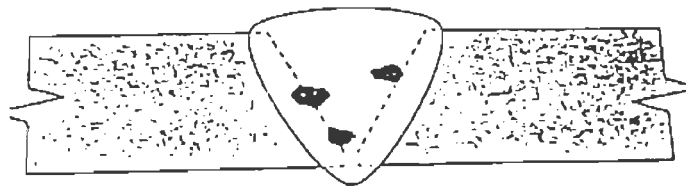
Inclusiones de tungsteno en la soldadura
